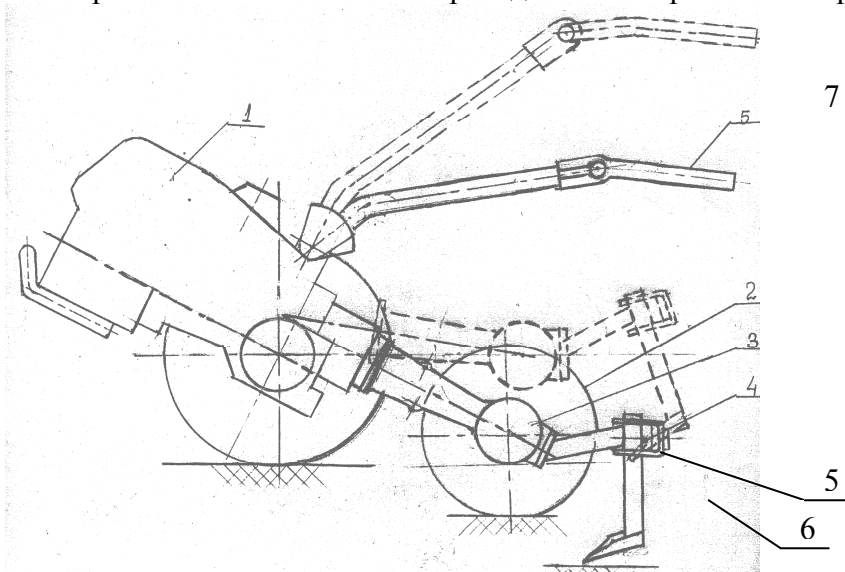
Комплексный мотоблочный агрегат для двухслойной обработки почвы
